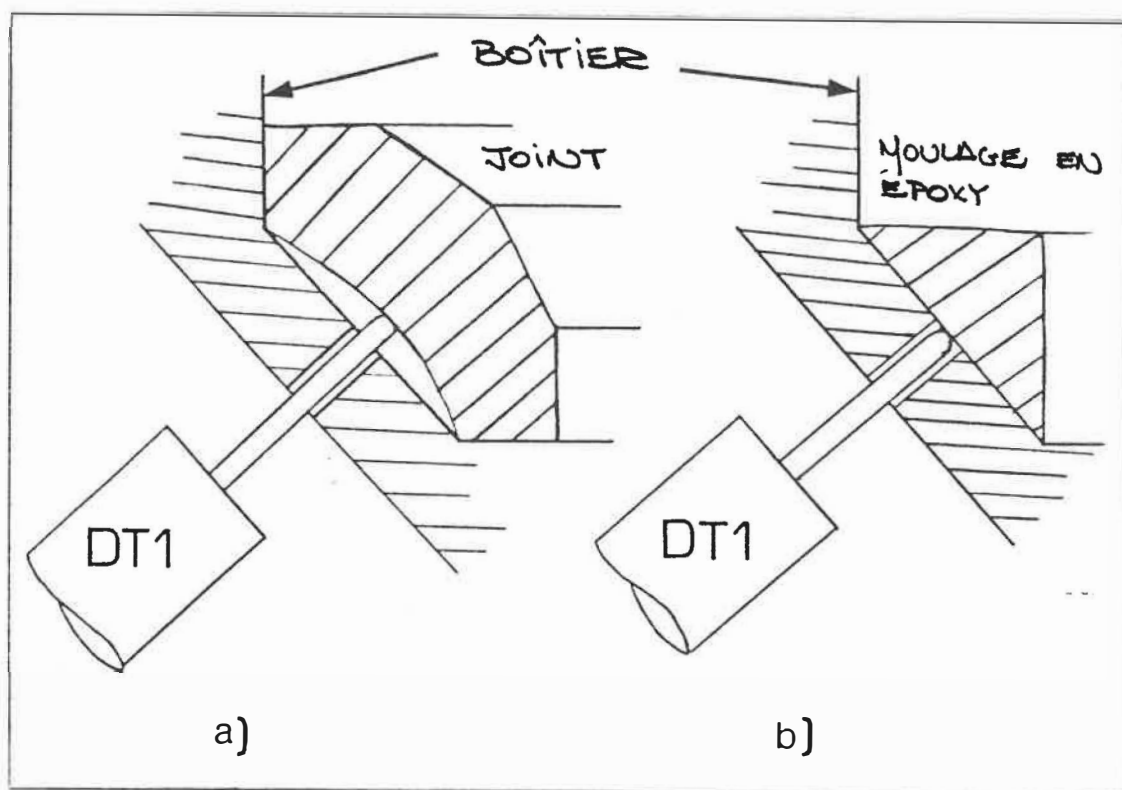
Coupe transversale d'un joint d'étanchéité;
